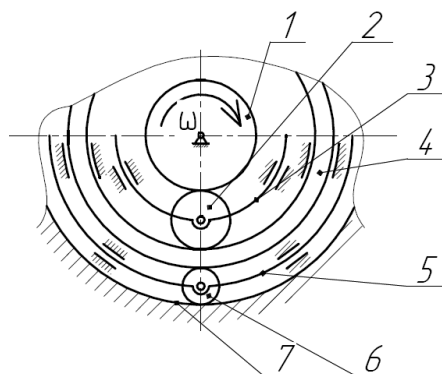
Кинематическая схема трехкольцевого подшипника:
